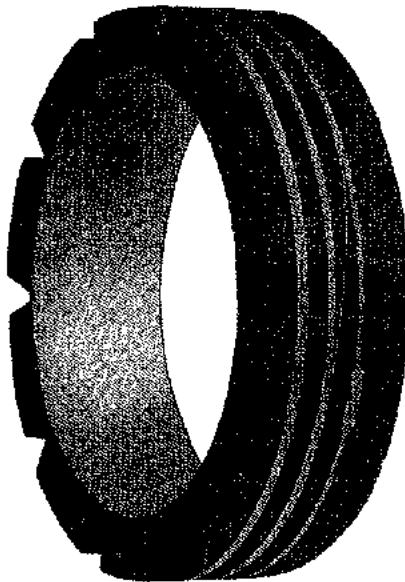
Muela de sectores (Blanchard Machine Co.)
